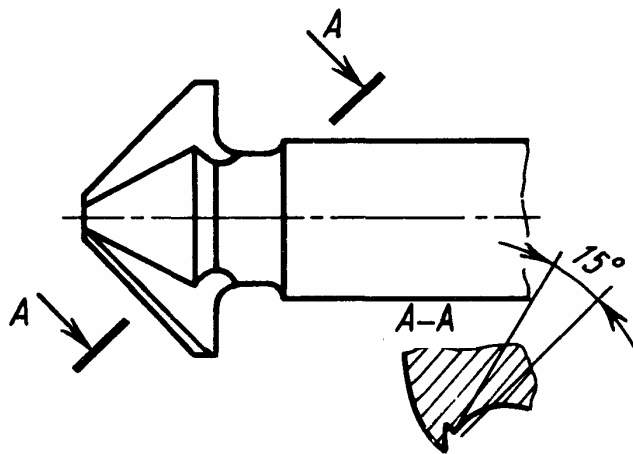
Зенківка з конічною поверхнею стружкових канавок
